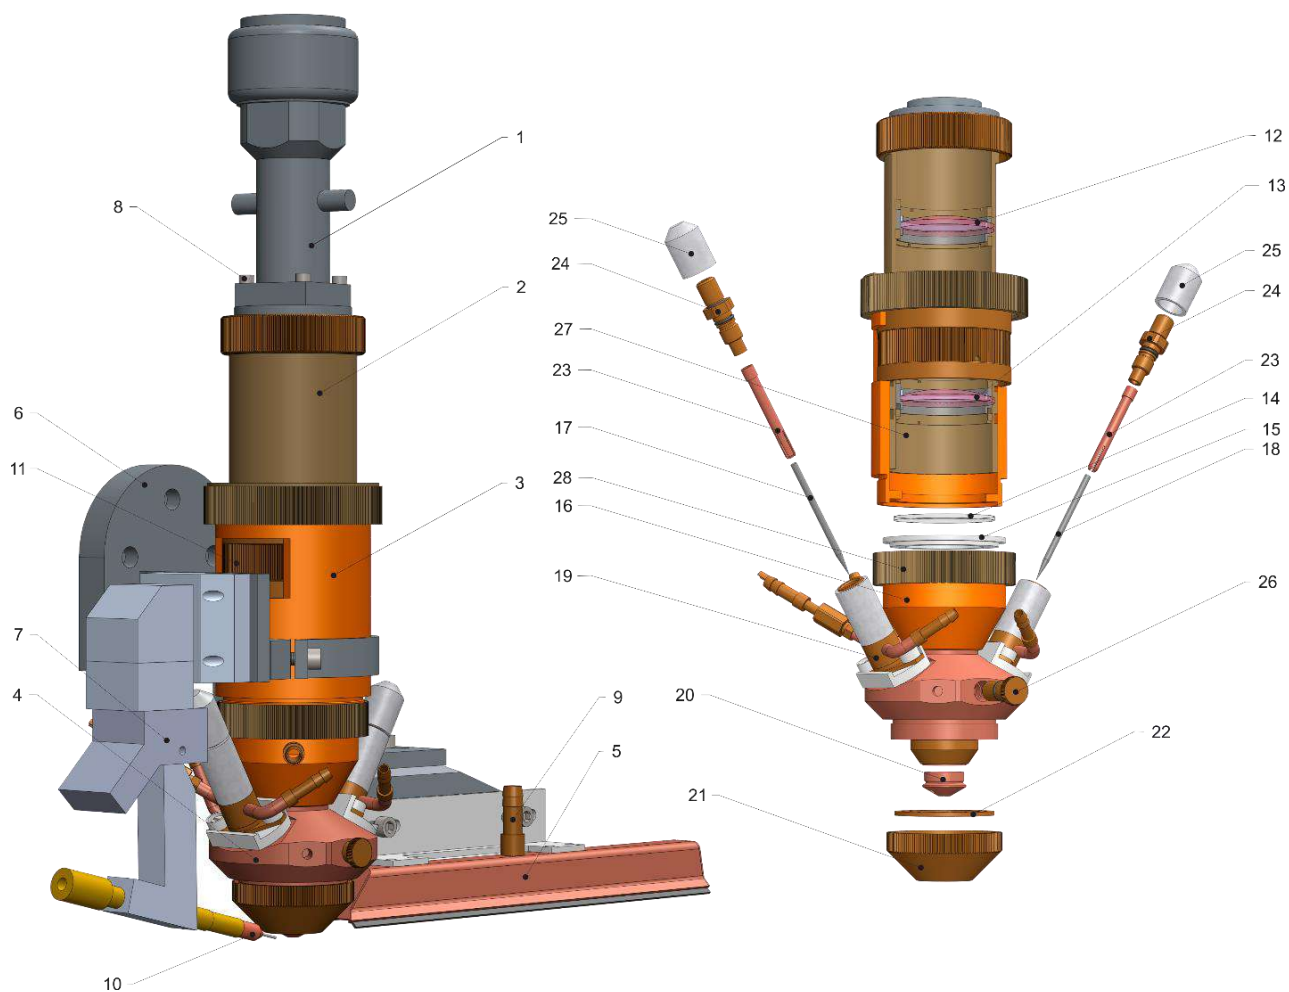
Схема конструкції інтегрованого плазмотрону установки для лазерно-мікроплазмового зварювання:
